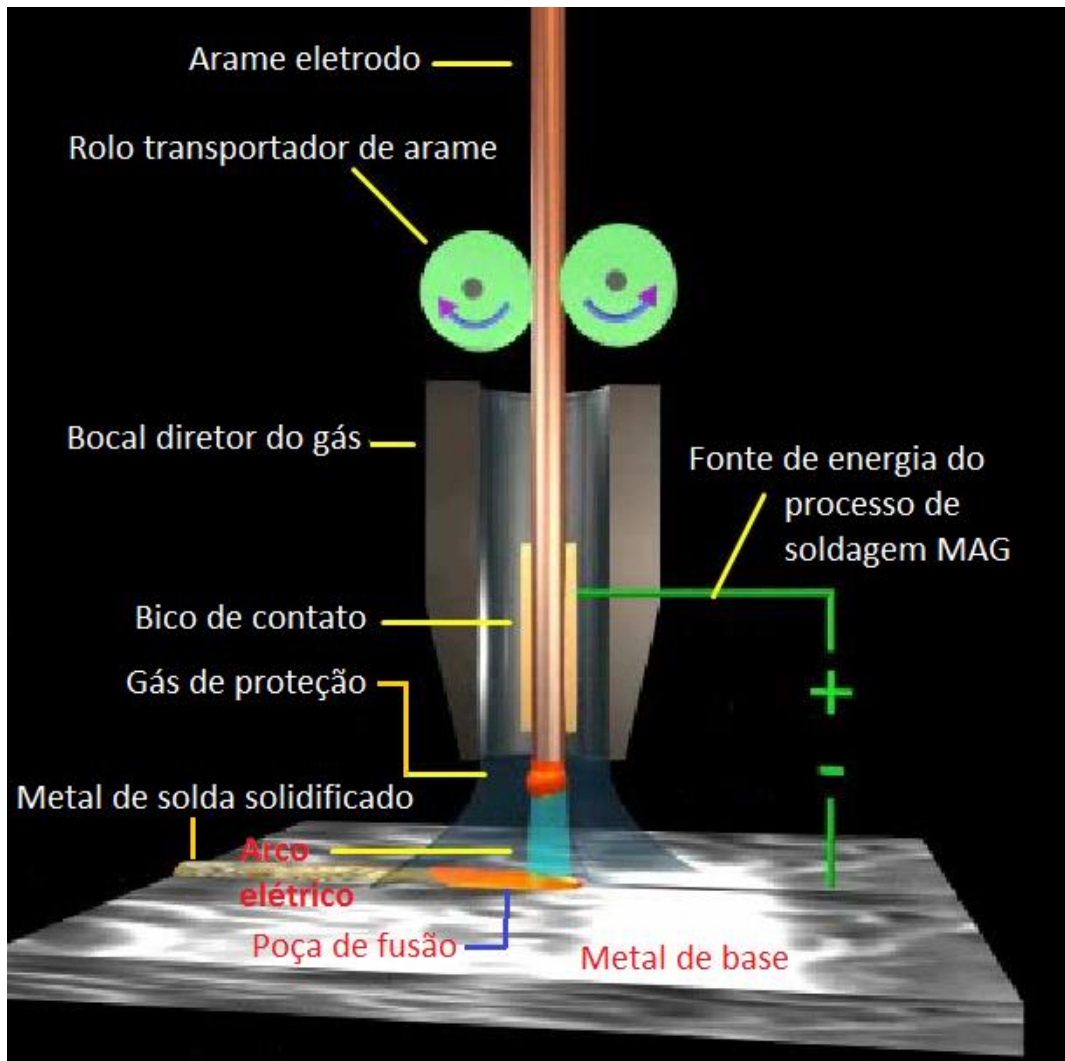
Processo convencional de soldagem MIG/MAG
